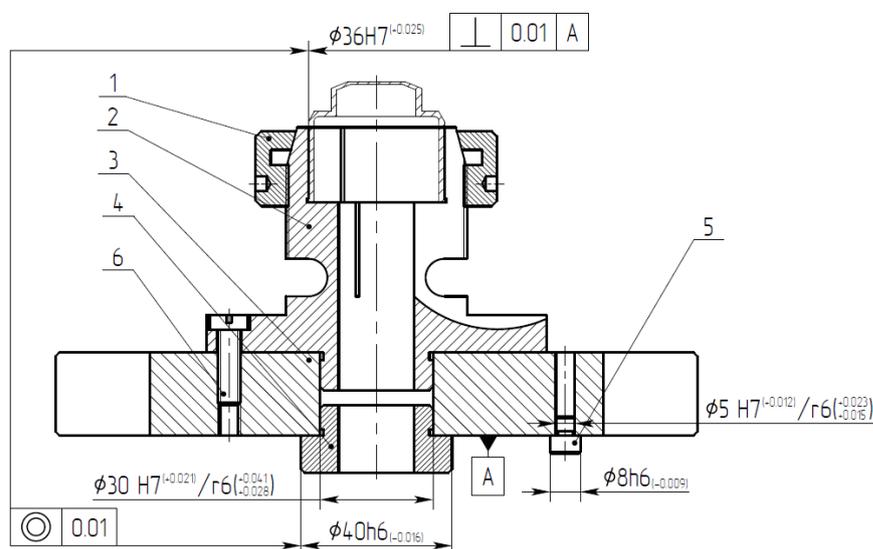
Станочное приспособление - Оправка зажимная для детали «Колпак»
